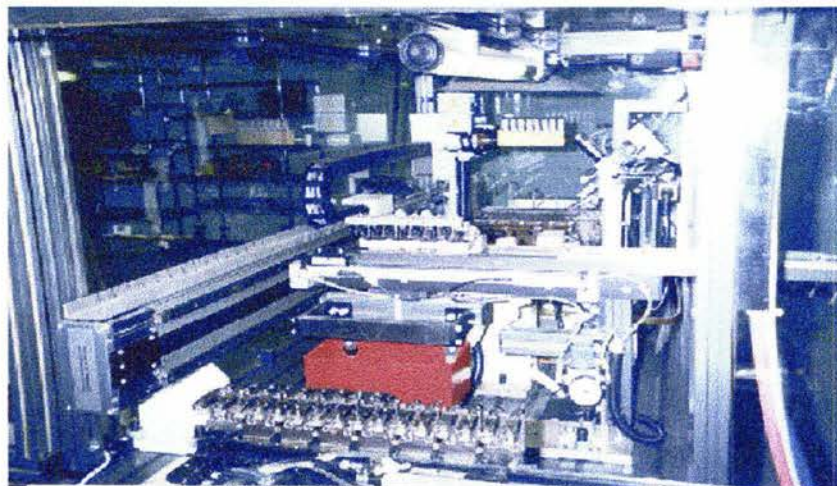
Máquina soldadora. (Cortesía de Midcom Inc.)
